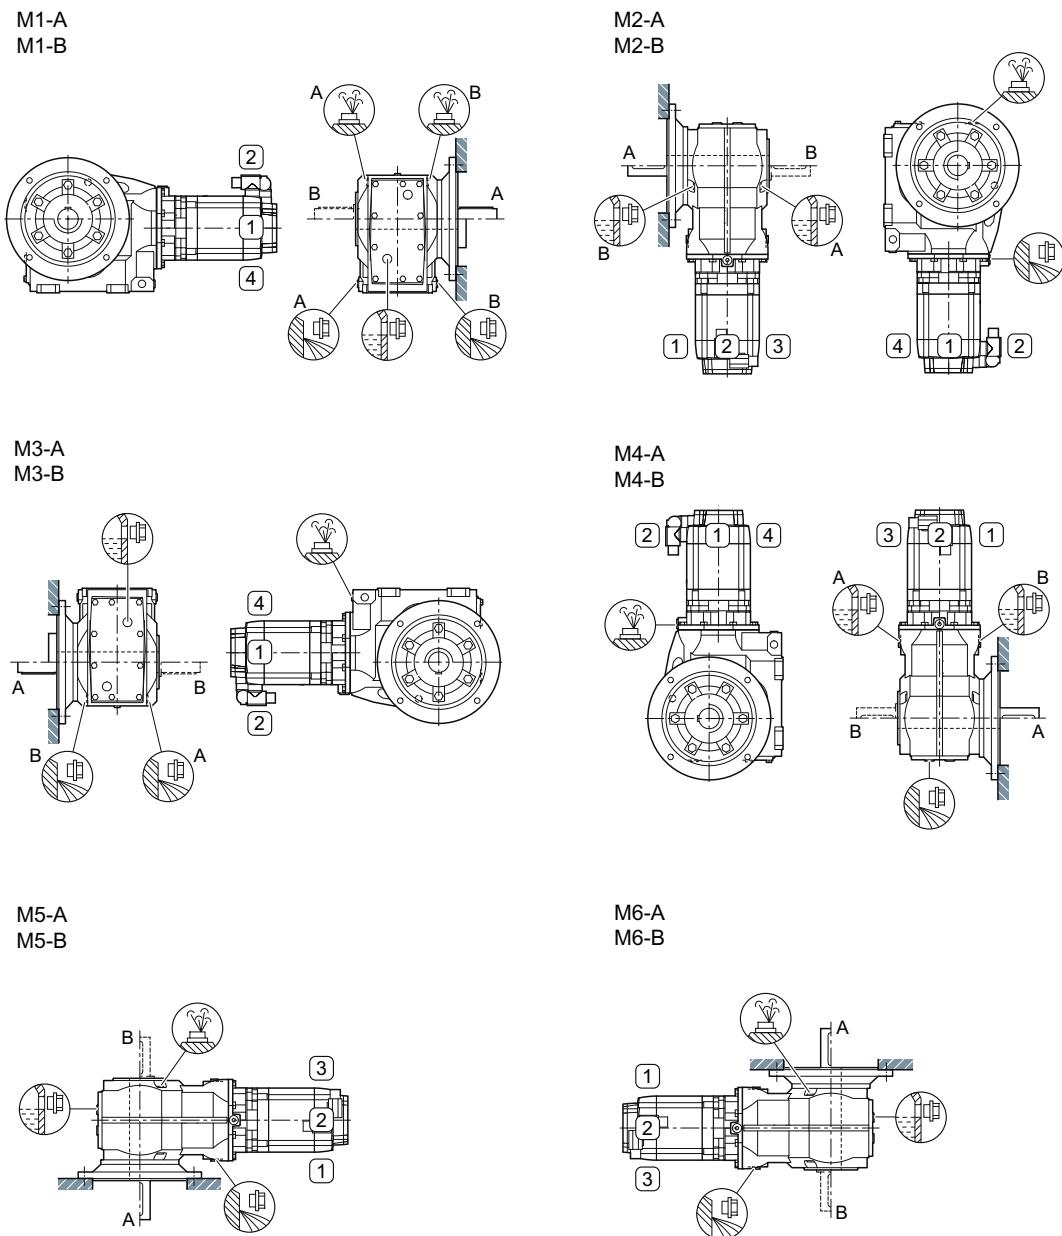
Einbaulagen für Servo-Kegelradgetriebemotor K.F (Flanschausführung) und KAZ (Gehäuseflanschausführung), Baugrößen 39 - 149, 3-stufig
